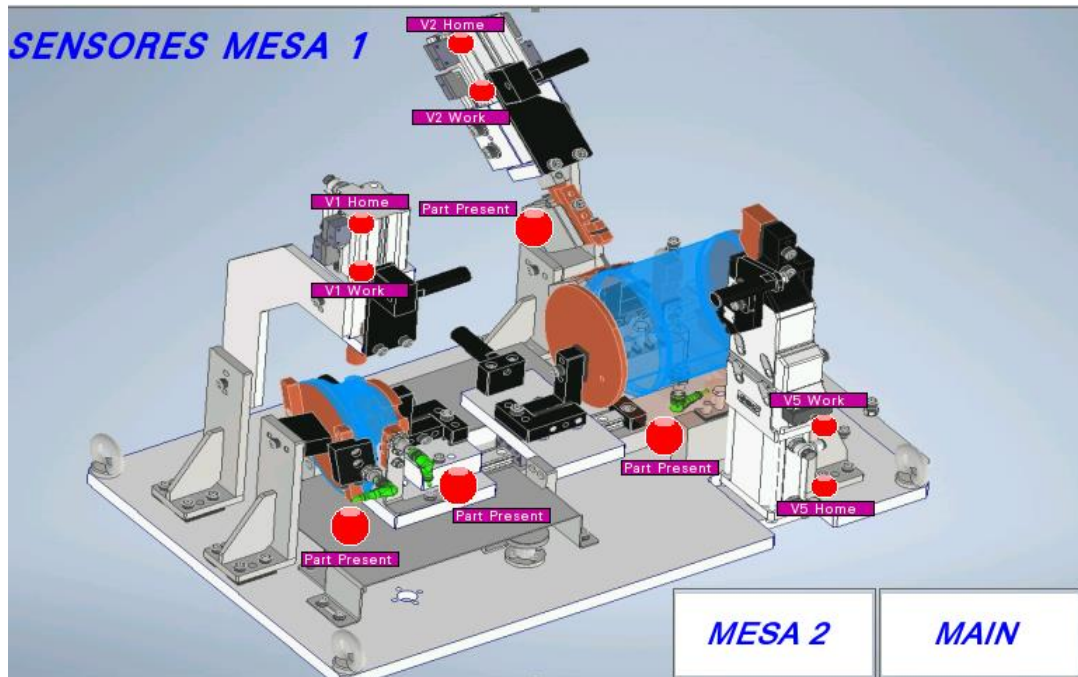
Layout completo mesa 1. Fuente. elaboración propia
